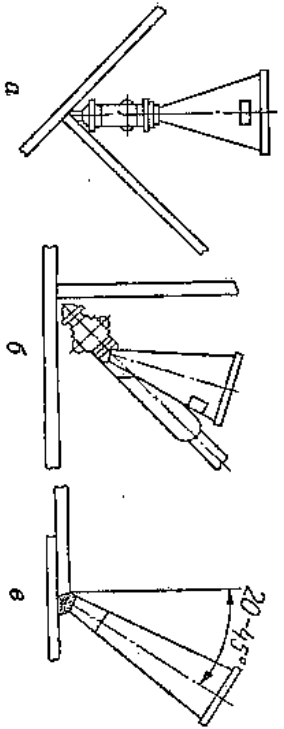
Схема полуавтоматической сварки под флюсом:
